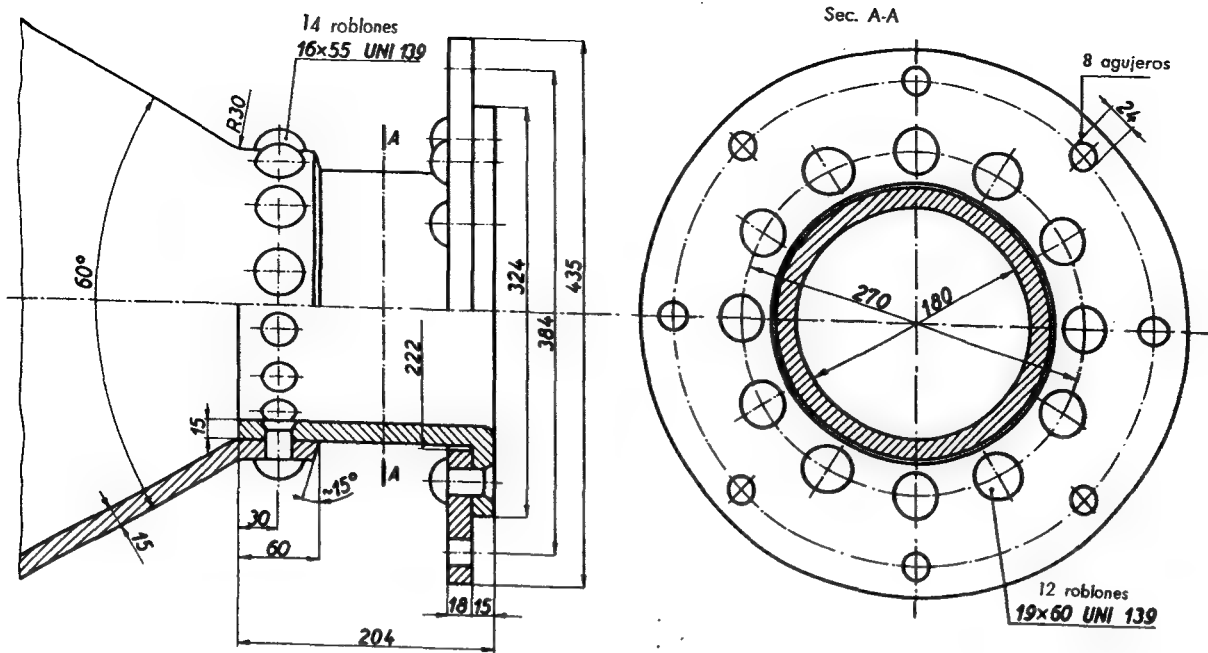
Detalles de una estructura con collarín y brida roblonados.
